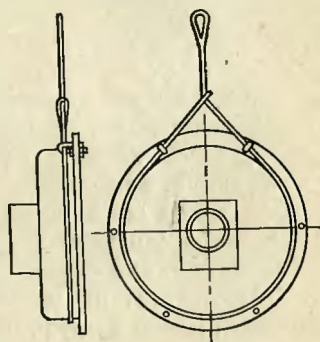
Строповка торцовой крышки «мертвой петлей»
